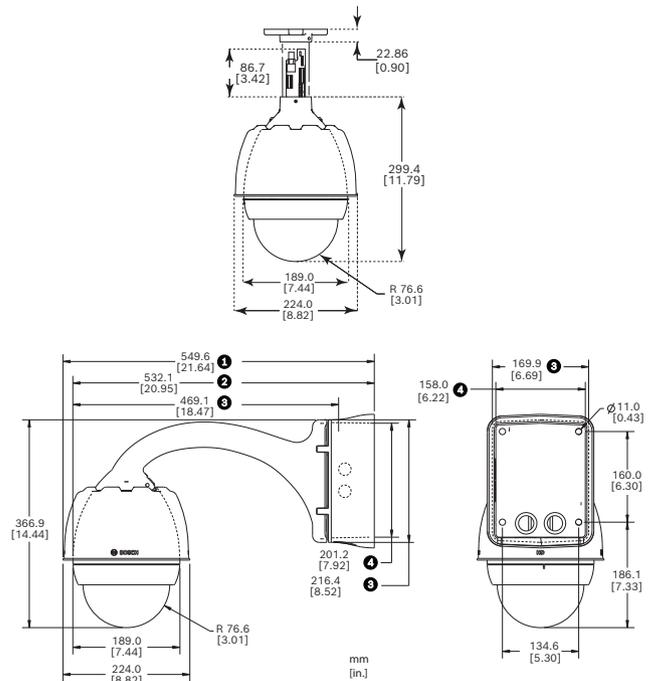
Dimensiones, montaje de techo AUTODOME 7000, montaje colgante
